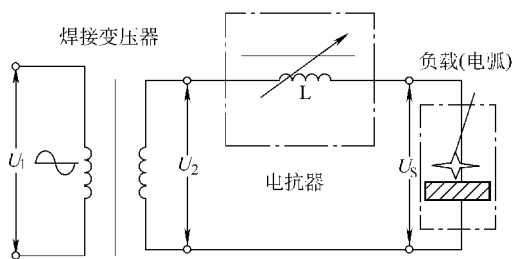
机械调节式工频交流埋弧焊电源主电路结构
